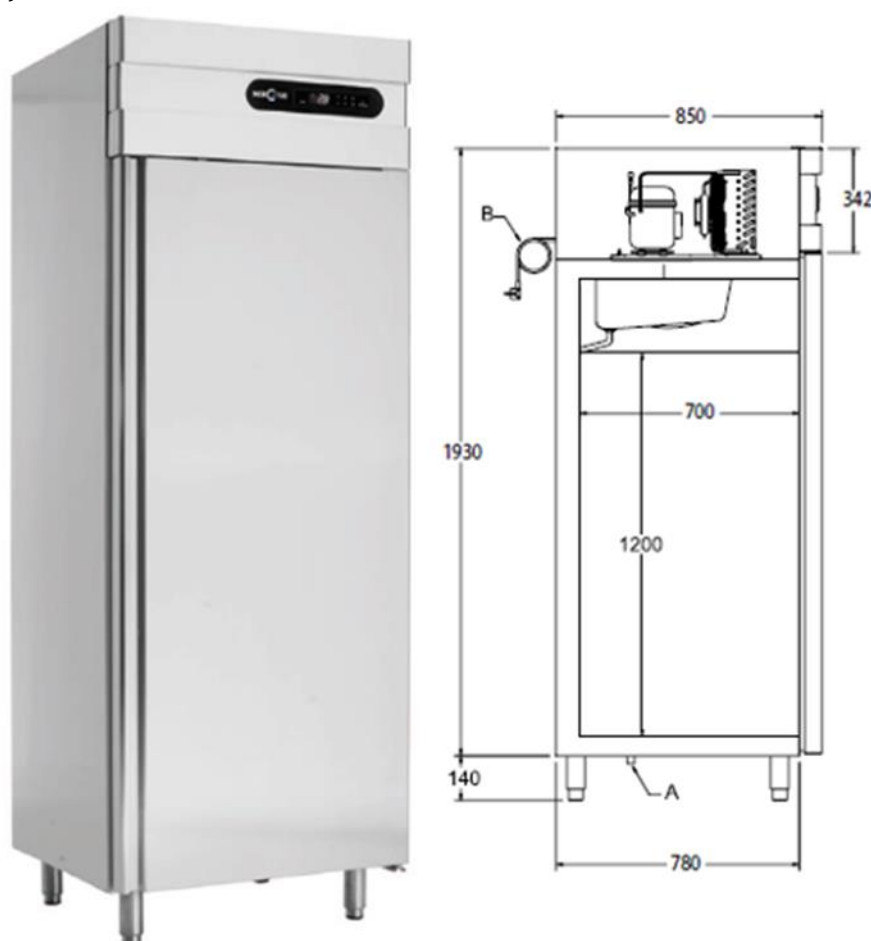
Design e dimensões do sistema de refrigeração considerado.
